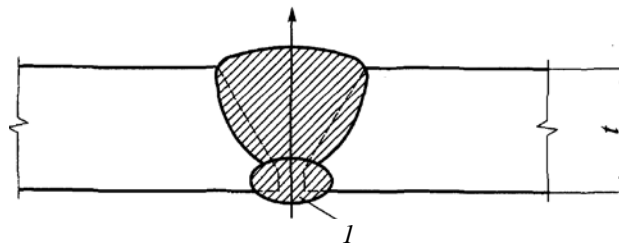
Зварне стикове з'єднання з підварюванням кореня шва
